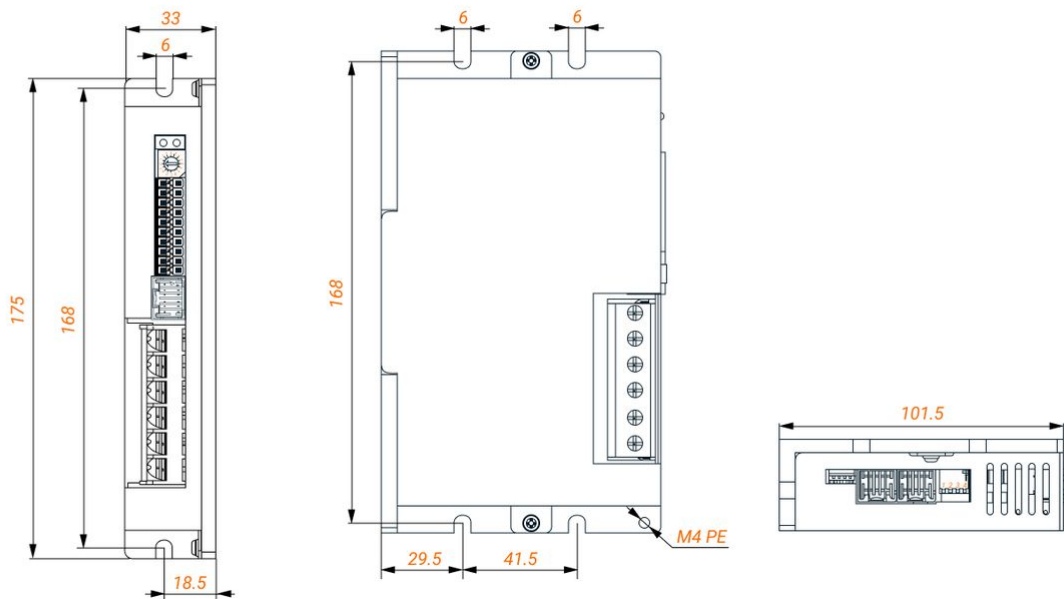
Габаритные размеры драйвера ELD2-RS7015B/7020B/7030B
